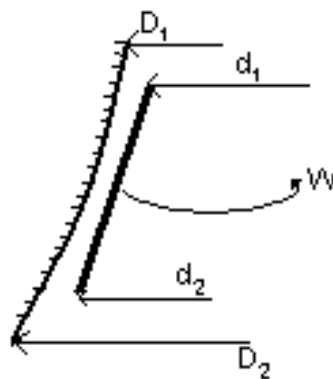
Конструкція з параболічною формою твірної кожуха та конічною формою твірної шнека
